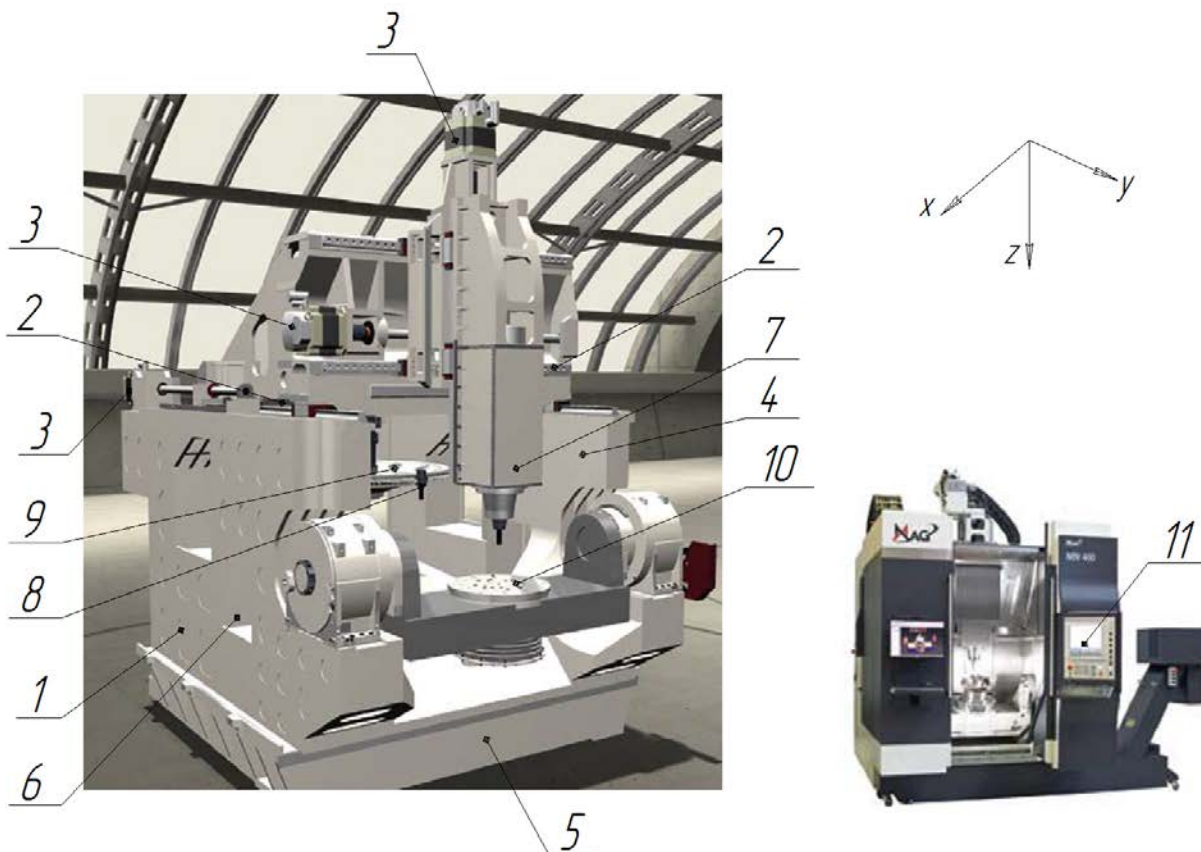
Компоновка, узлы и основные направления движения обрабатывающего центра MAG NVB 400
